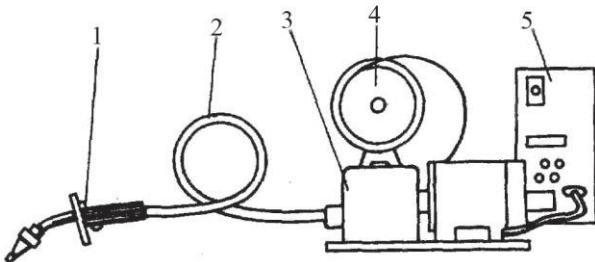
Схема полуавтомата для дуговой сварки
